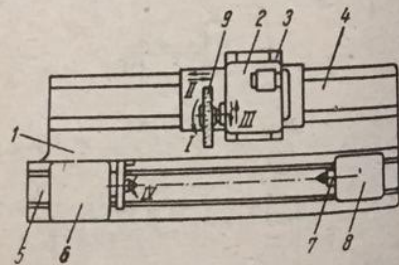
Mașină de rectificat rotund exterior la care avansul longitudinal este executat de sculă.
